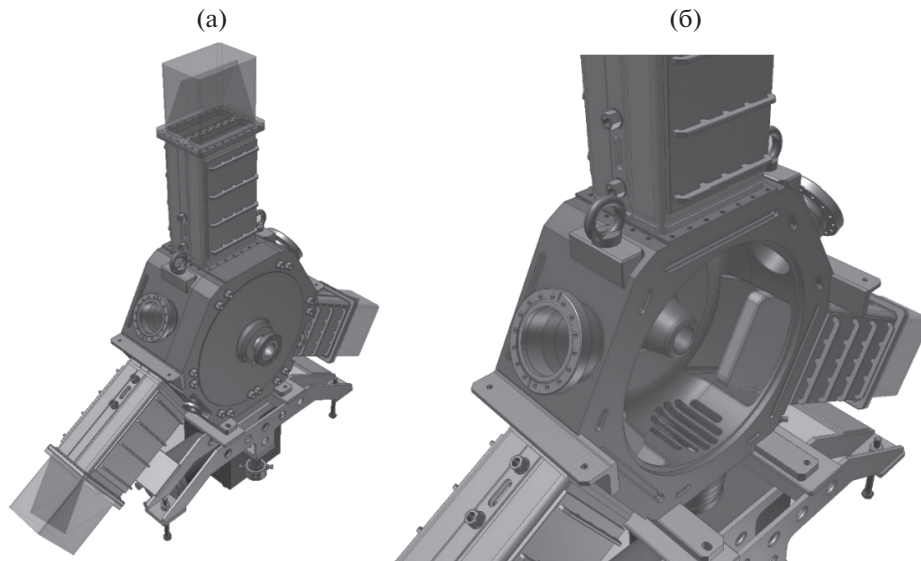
3D-модель резонатора: а – резонатор в сборе, б – без торцевой стенки.
